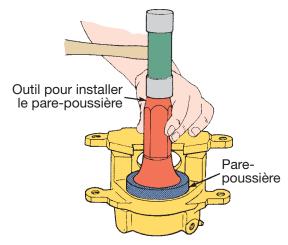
Positionner un pare-poussière avec un outil d'installation à pare-poussière.
